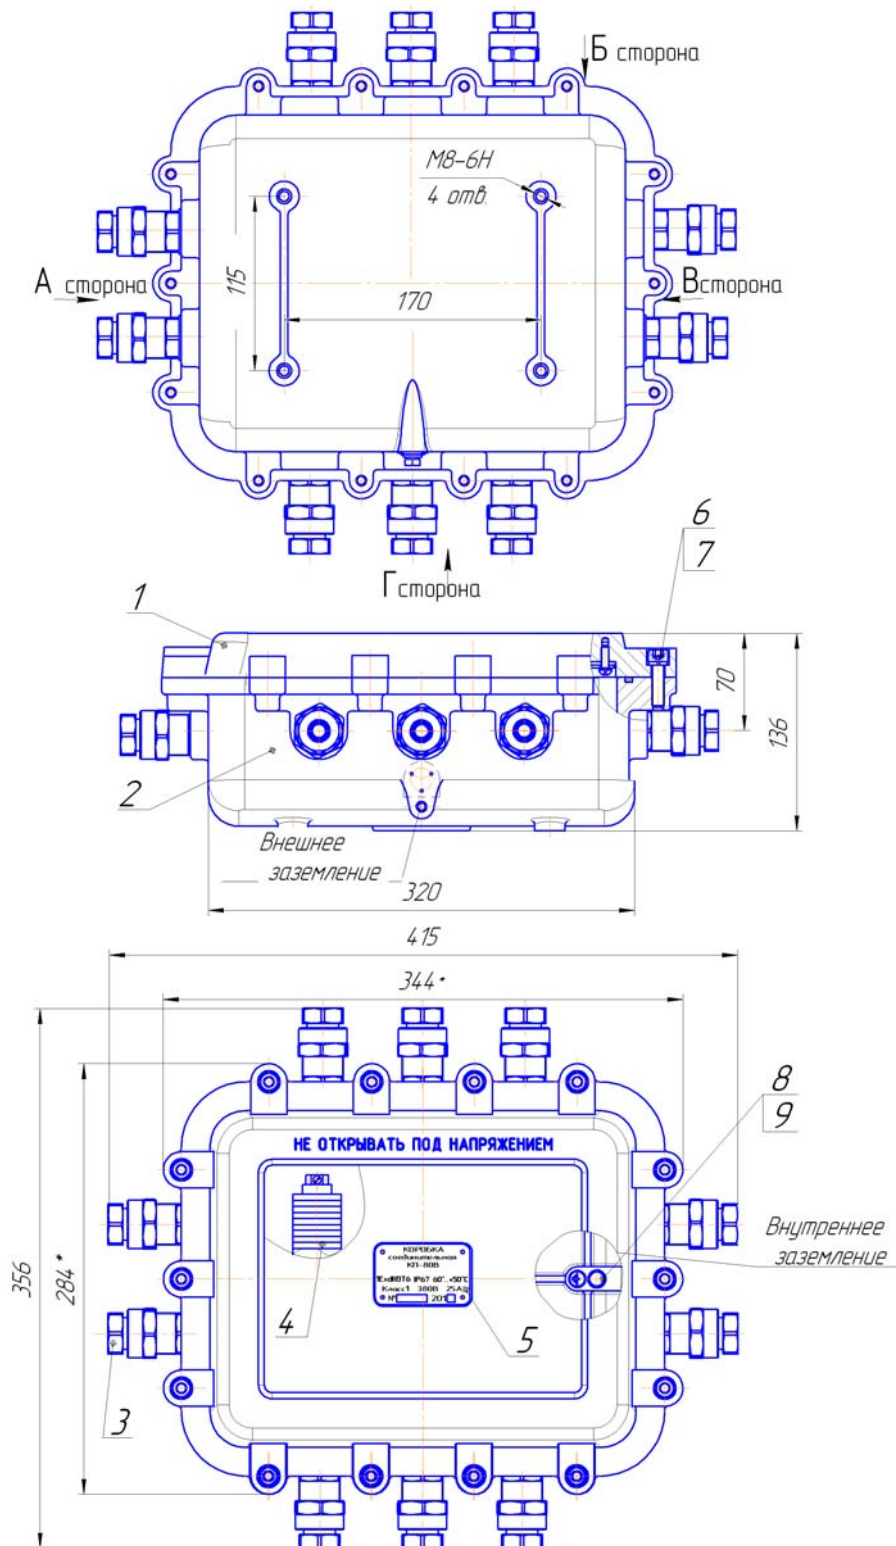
Состав и присоединительные размеры коробки соединительной КП-16В-00-(2)-32-04-БЗГЗ-G3/4-00-0X-16 ТУ 3424-003-75666544-2007
